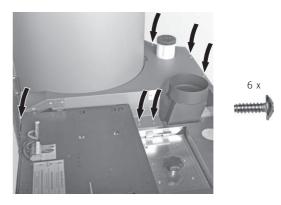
Fissare il rivestimento con 6 viti autofilettanti
